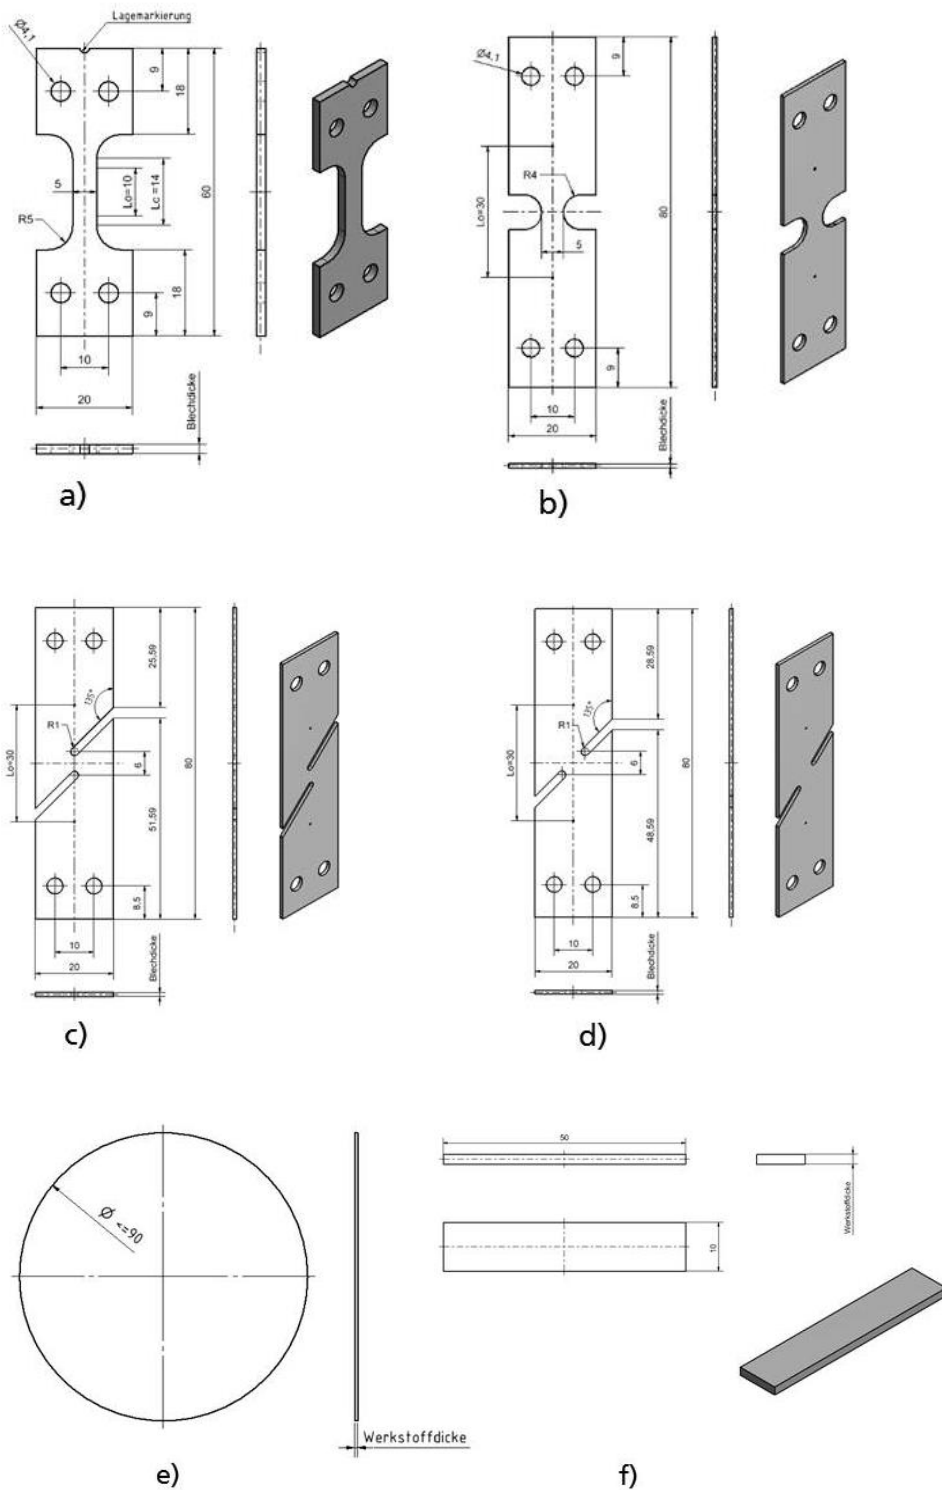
Verwendete Probengeometrien a) Glatzzugprobe, b) Kerbzugprobe, c) Scherzugprobe  $\theta = 0^\circ$ , d) Scherzugprobe  $\theta = 45^\circ$ , e) Durchstoßprobe, f) Biegeprobe
